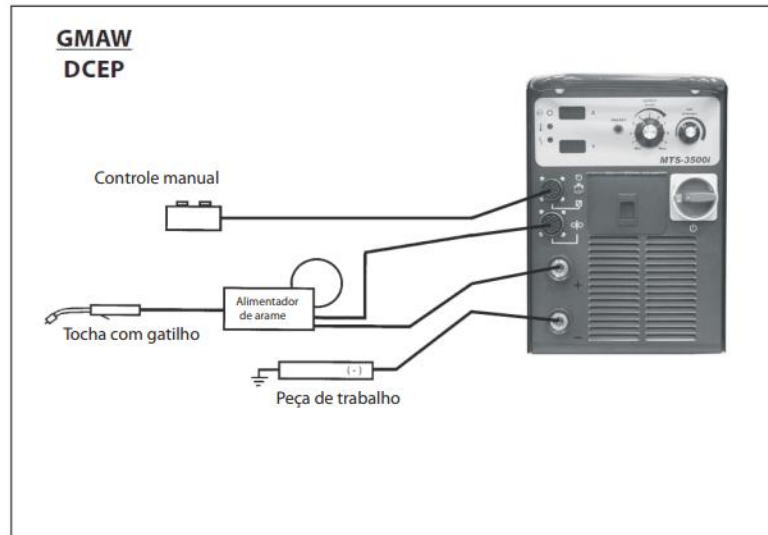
Máquina de Solda MTS-3500i - Fonte: Manual Eutectic Castolin
